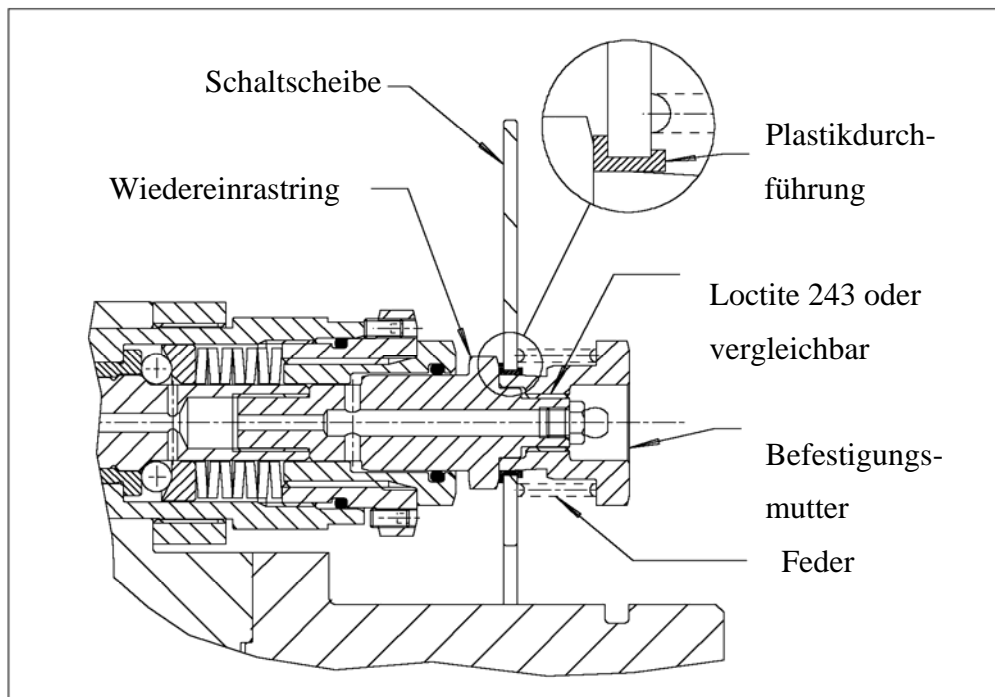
Einbaubeispiel für Ausführung mit Schaltscheibe
